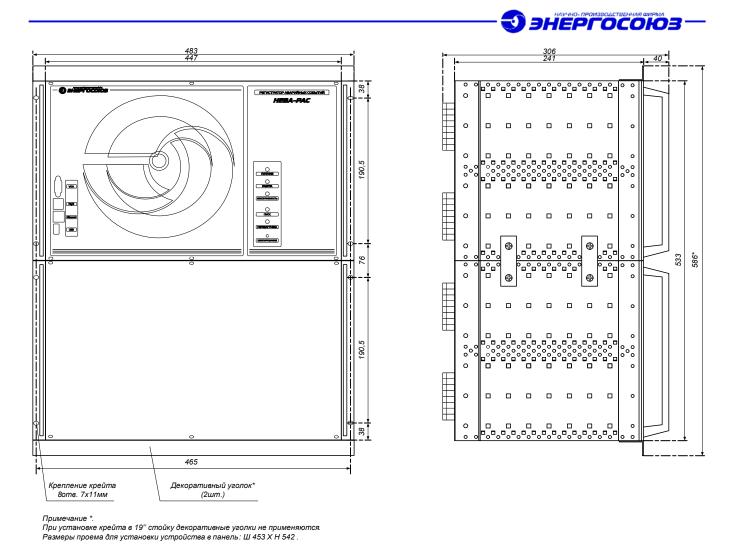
Габаритный чертёж PAC19-2.12U с установочными размерами
